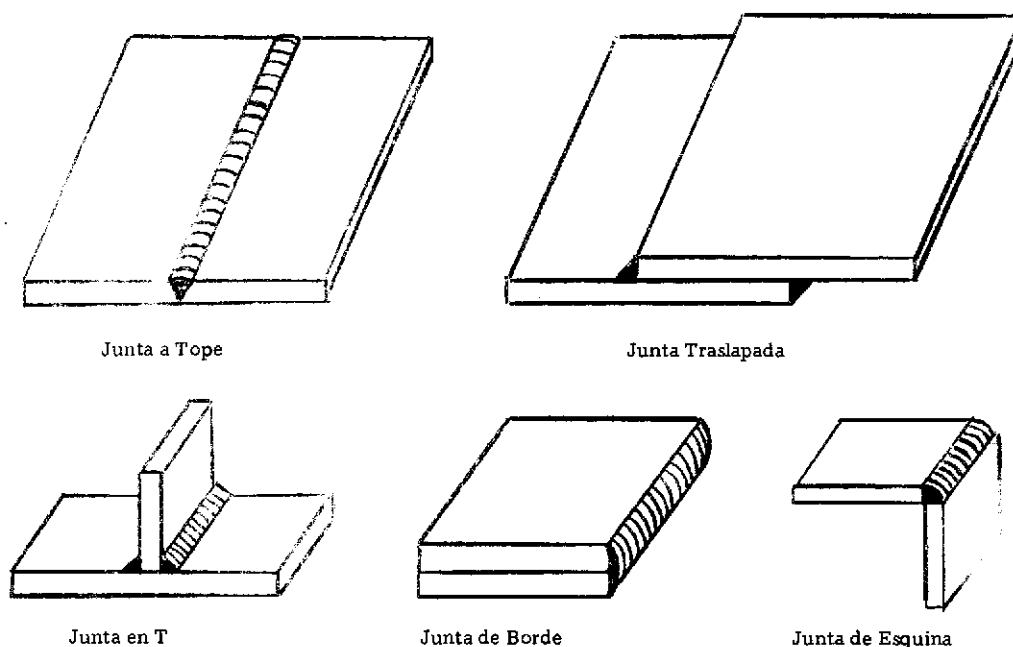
Tipos de juntas soldadas.
